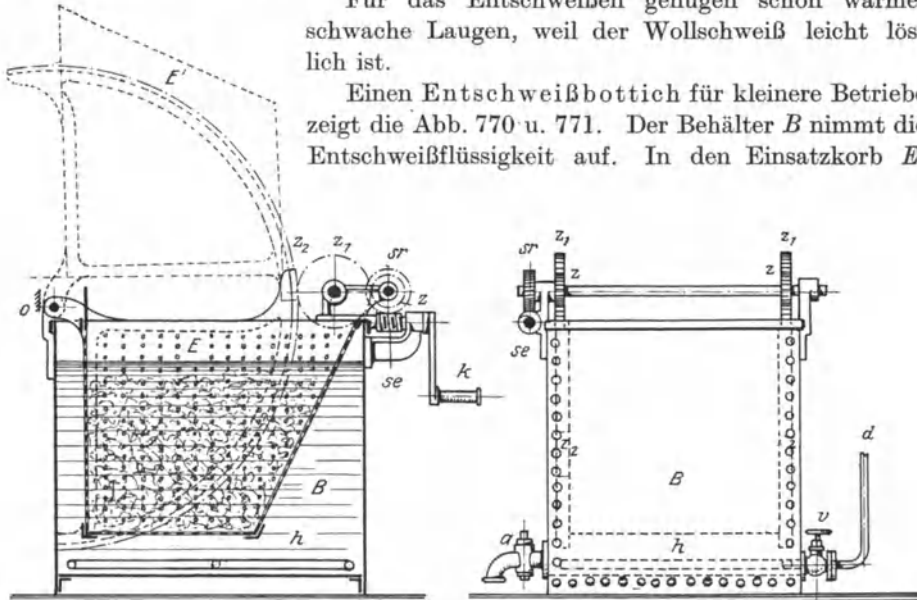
u. 771. Woll-Entschweißbottich.
